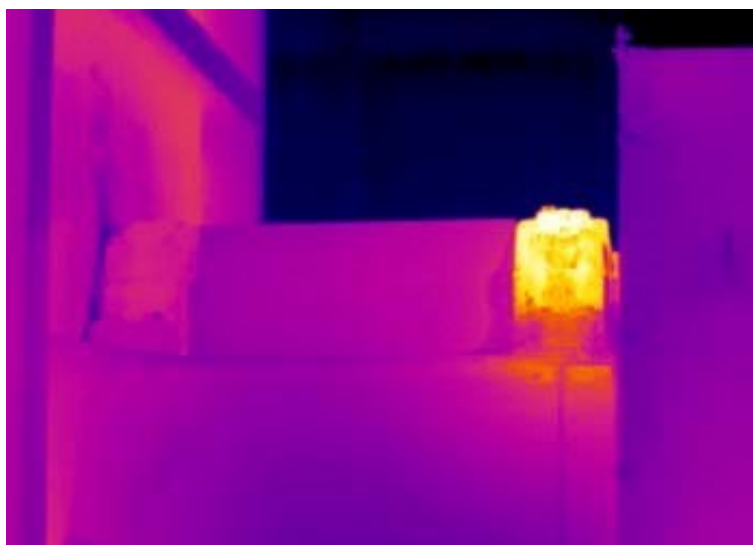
Гаряча точка на корпусі підшипника
